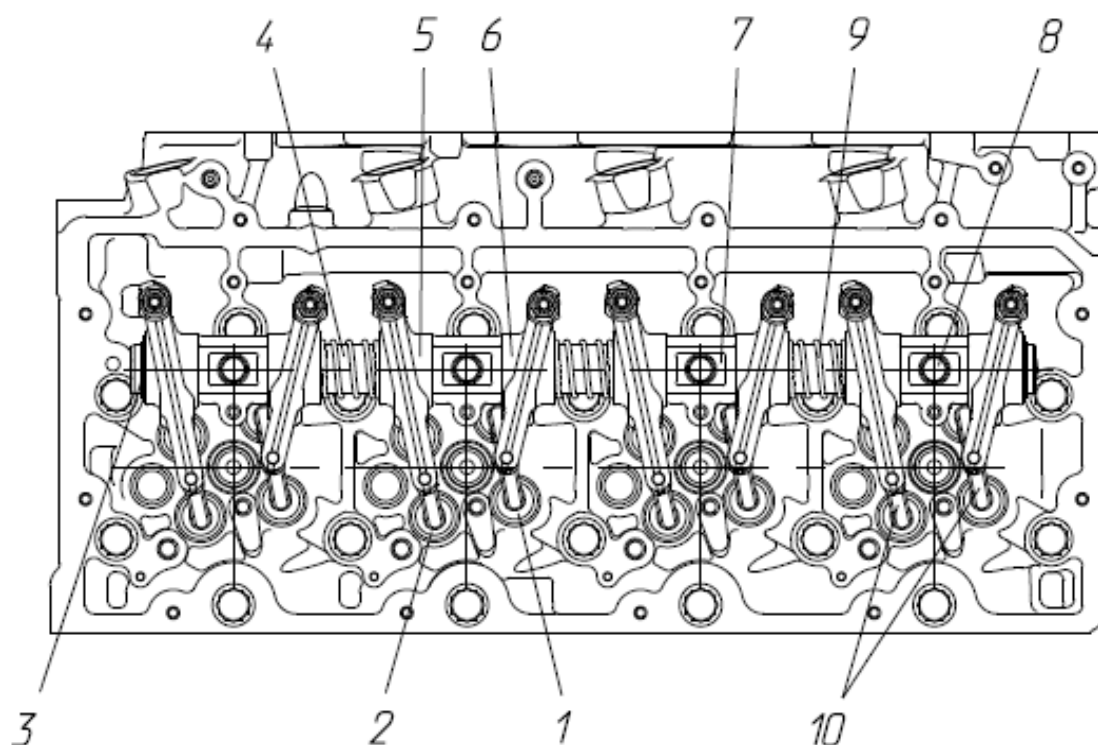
Вид сверху на механизм газораспределения, установленный в головке цилиндров:
